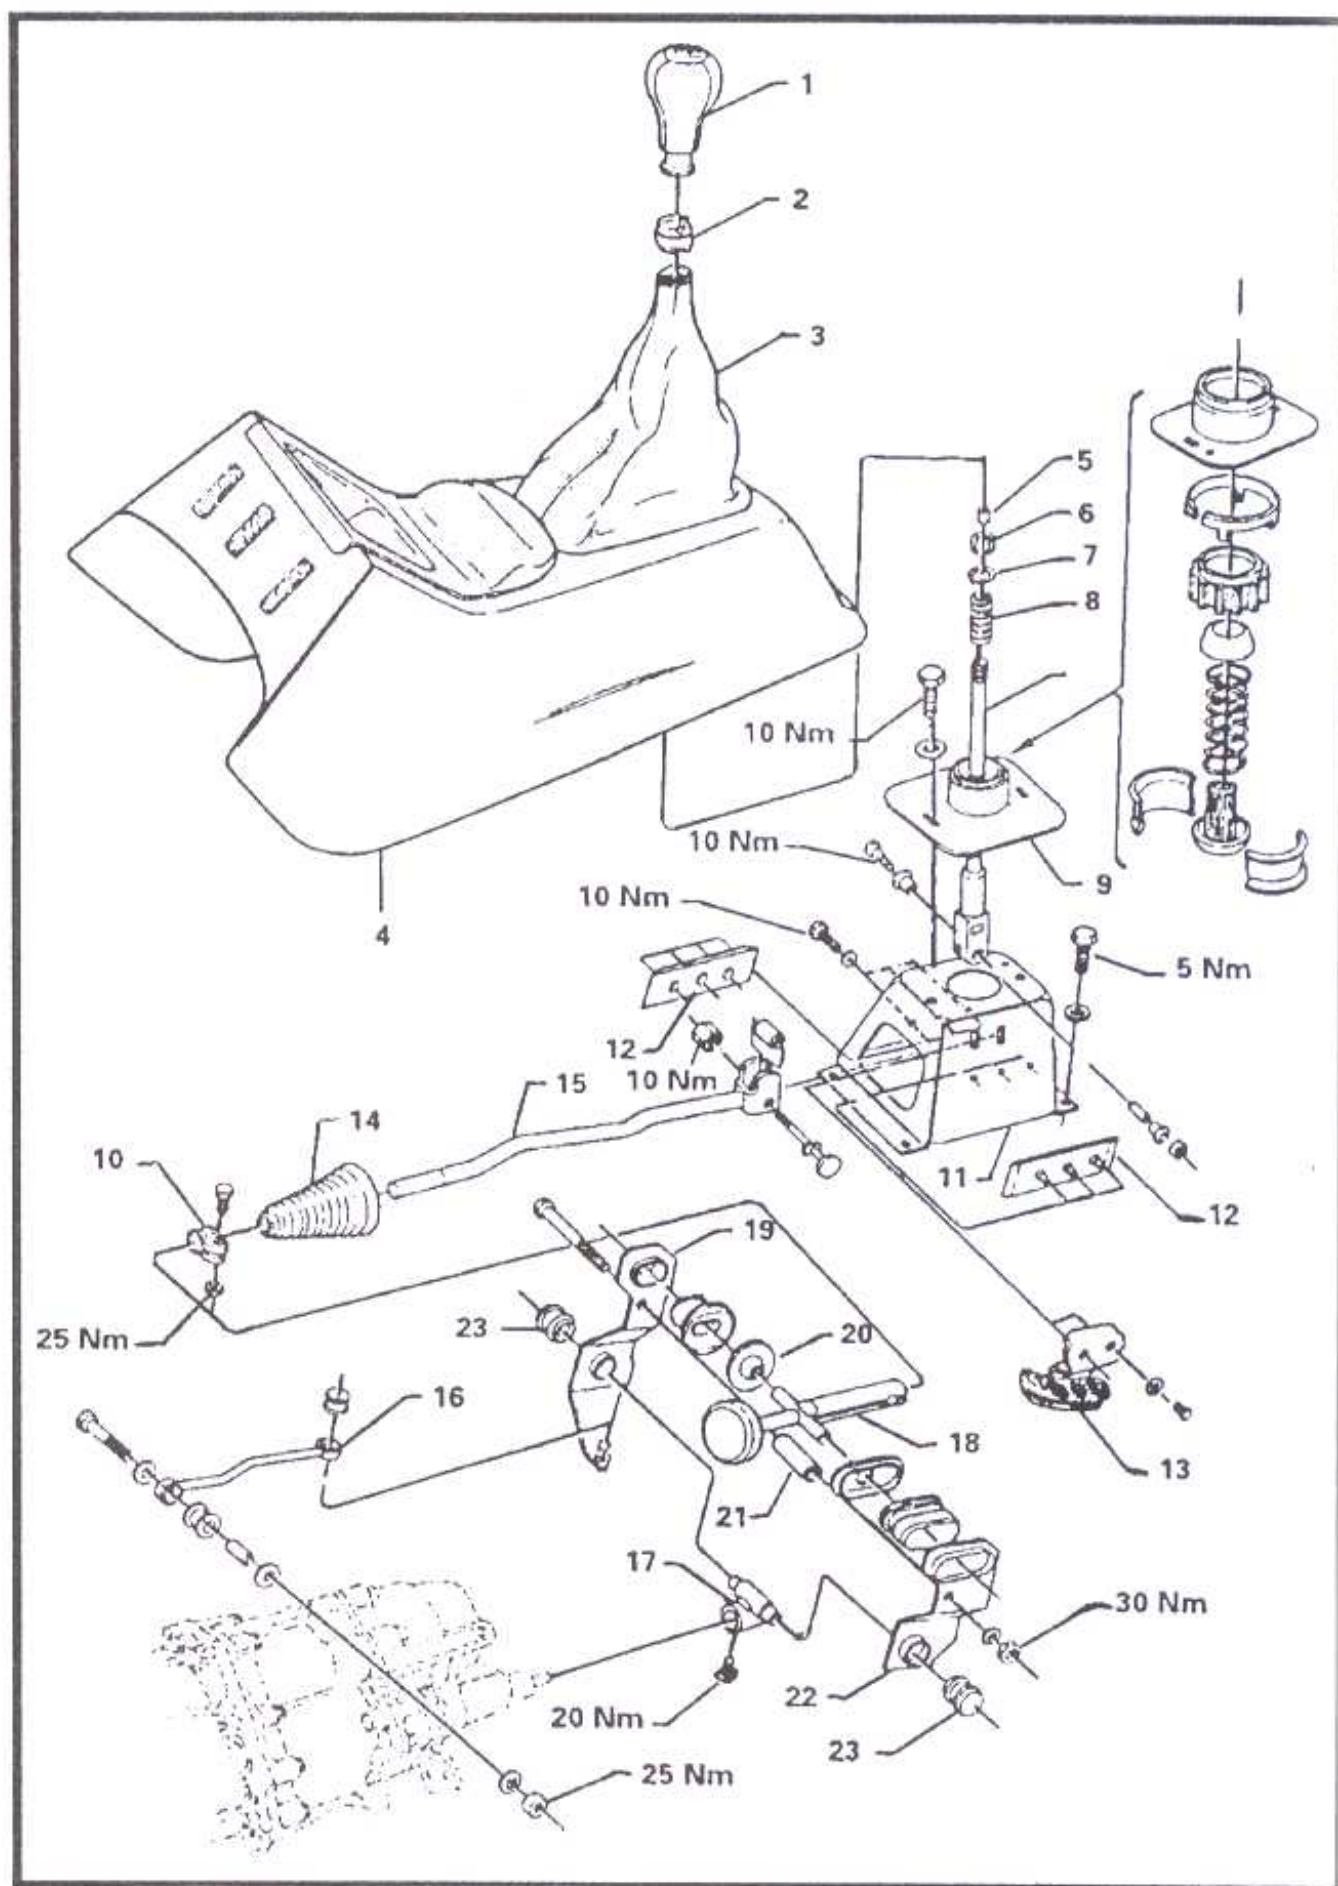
Despiece del sistema de la palanca de cambios.
